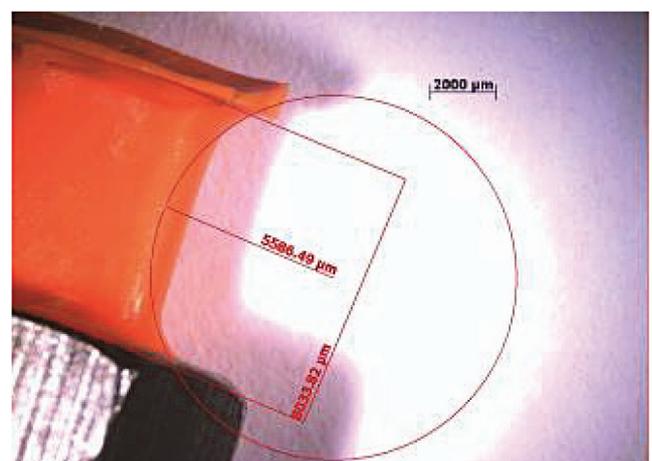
Схема измерения радиуса закругления рабочей поверхности канала (вид правой стороны проекции слепка канала фильеры)
